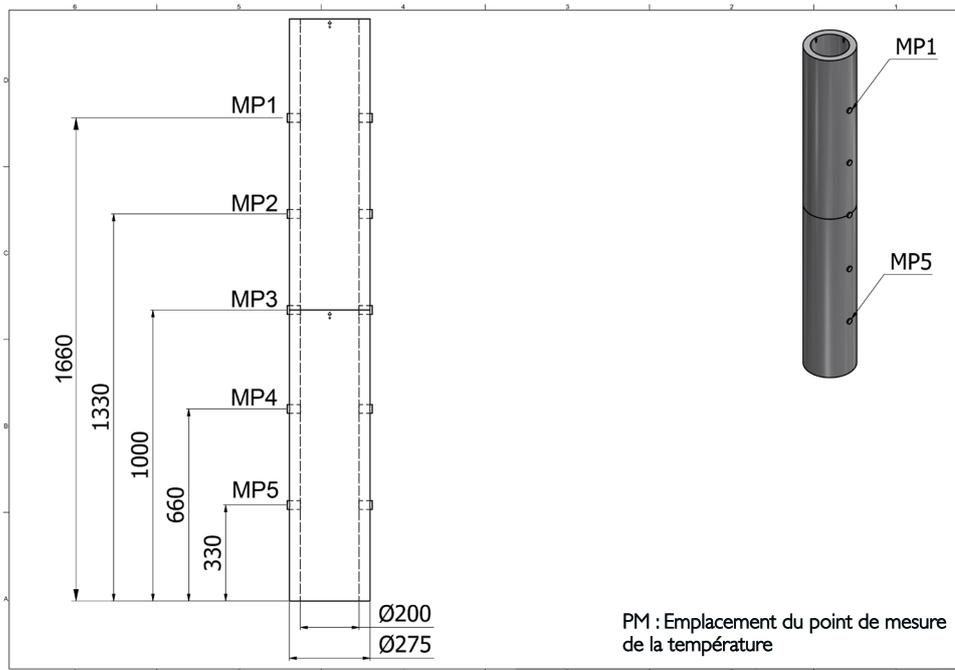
Dessin technique des points de mesure thermique sur le tube extérieur des éléments de compteur AT
